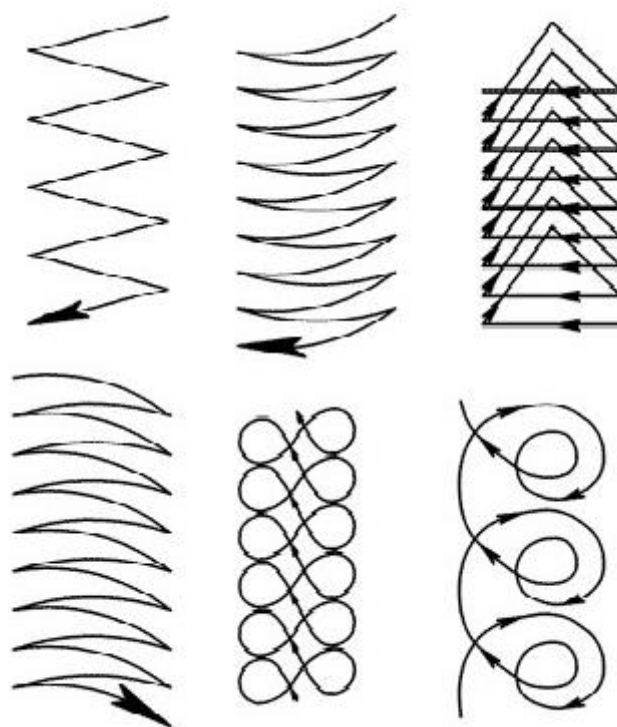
Движения покрытым электродом при сварке.
